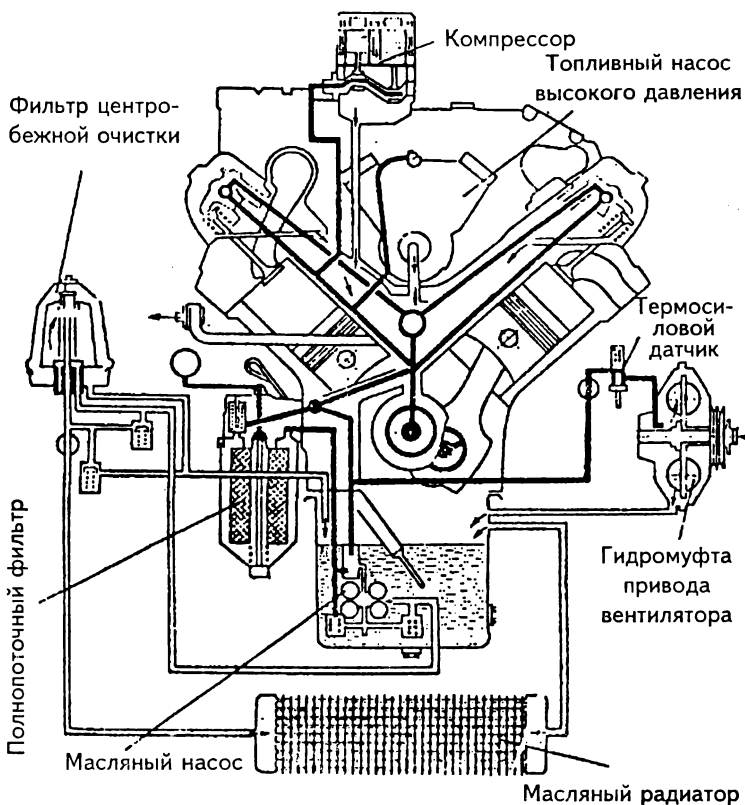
Схема системы смазки двигателя КамАЗ-740
